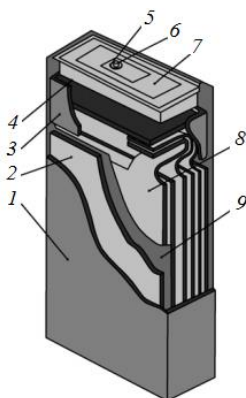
Конструкція Ni-MH акумулятора: 1 – корпус; 2 – негативний електрод; 3 – ізолятор; 4 – ізоляційна прокладка; 5 – ковпачок клапана; 6 – датчик тиску; 7 – кришка; 8 – позитивний електрод; 9 – сепаратор
